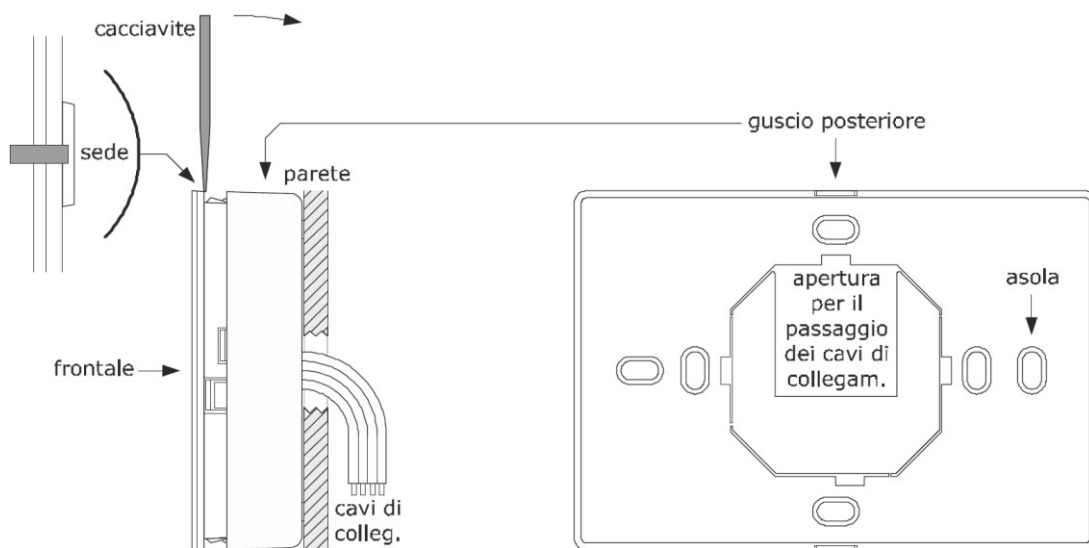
Dimensioni per fissaggio controllo remoto COLOR-TOUCH
